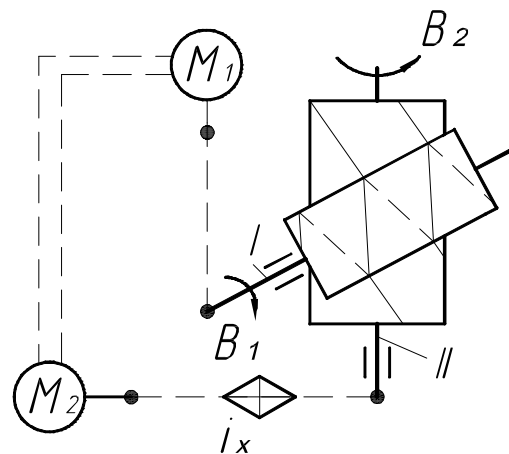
Структурная схема цепи обката зубошлифовального станка с синхронными двигателями
